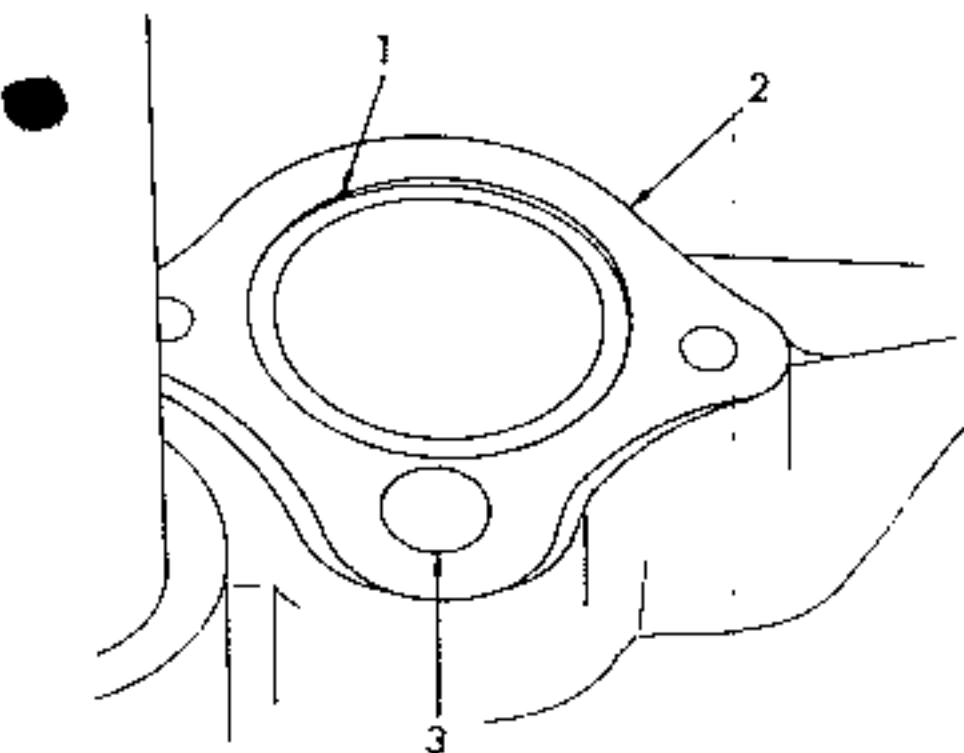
Ansicht der Öffnung für den Thermostat beim V8-Motor.
